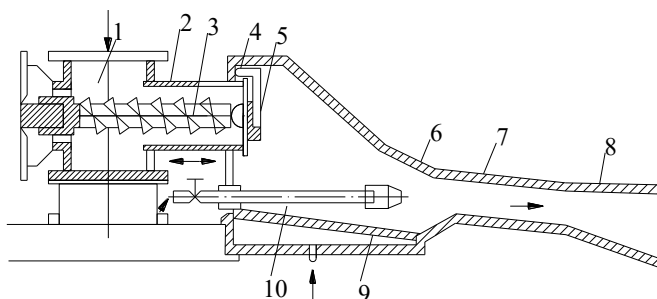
Схема пневматического винтового насоса ТА-14А с эжекционной насадкой: 1– приемная камера; 2 – гильза; 3 – напорный шнек; 4– смесительная камера; 5 – обратный клапан; 6 – конфузор; 7 – смесительный участок; 8 – диффузор; 9 – микропористая перегородка аэроднища; 10 – сопло; 1 1 – электродвигатель
